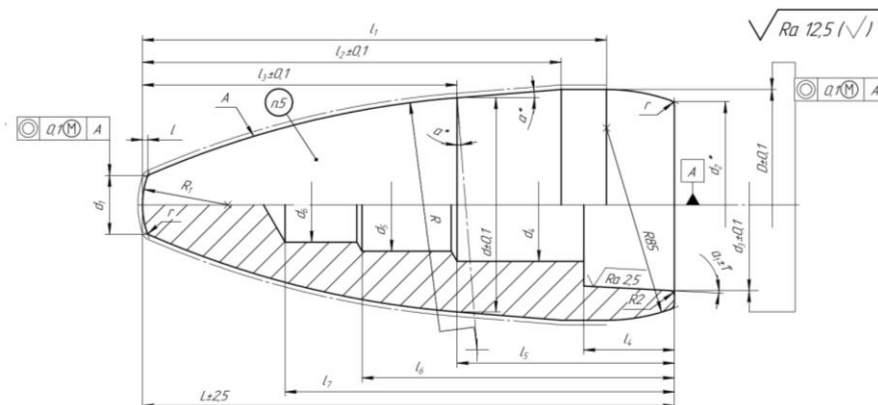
Новая калибровка оправки для удлиненной бочки валка
